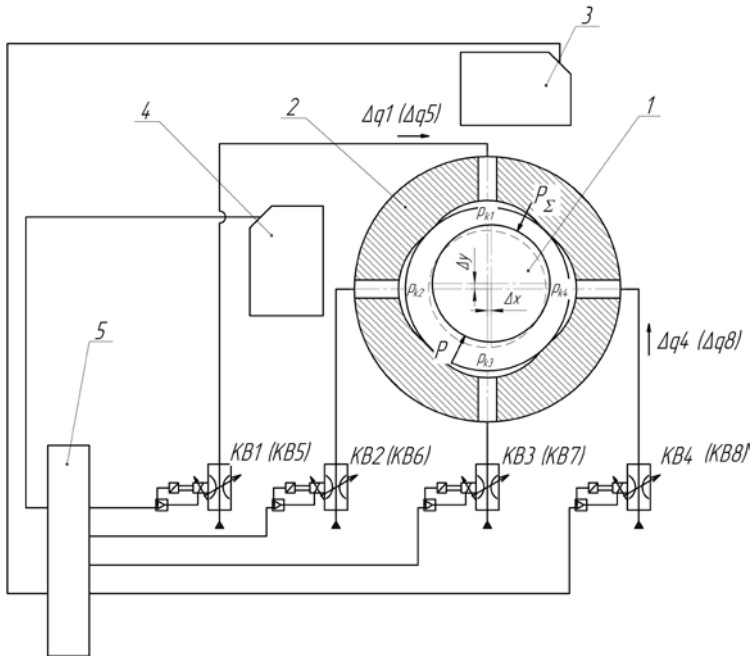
Схема автоматичного регулювання положенням шпинделя
